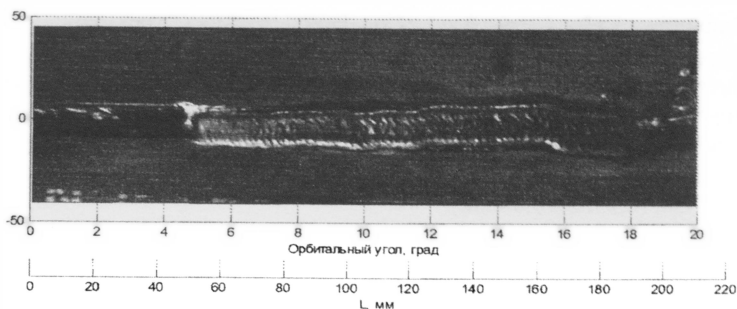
Развертка поверхности сварного шва кольцевого стыка.
